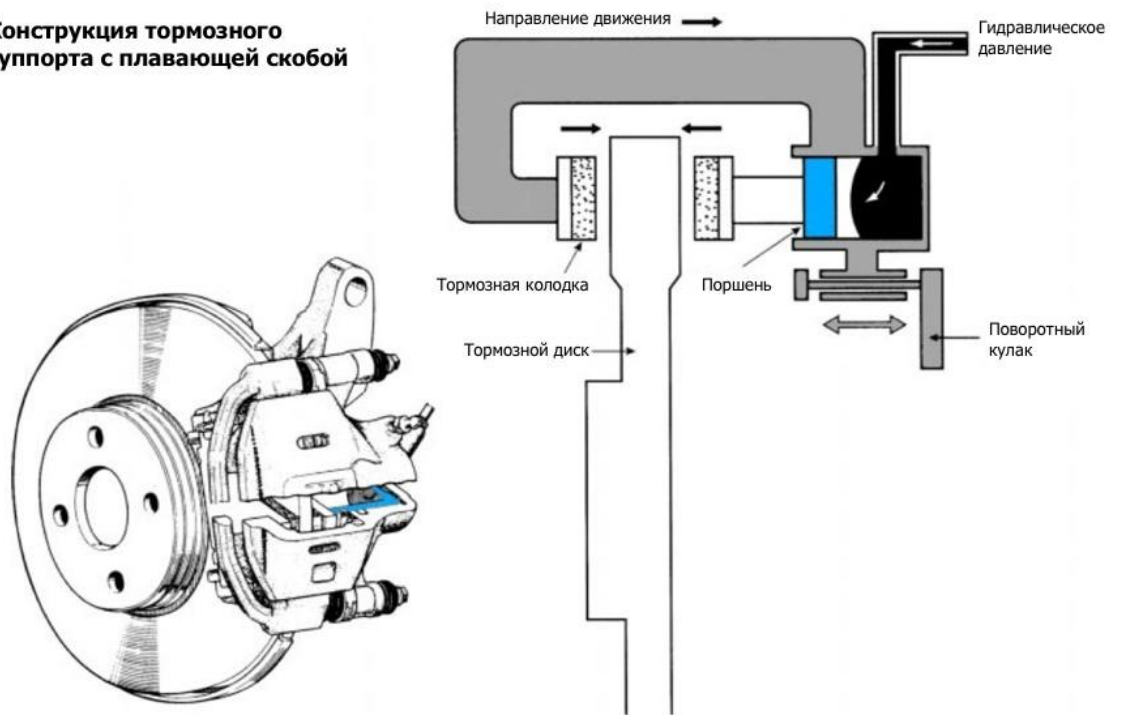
Конструкция суппорта с плавающей скобой
